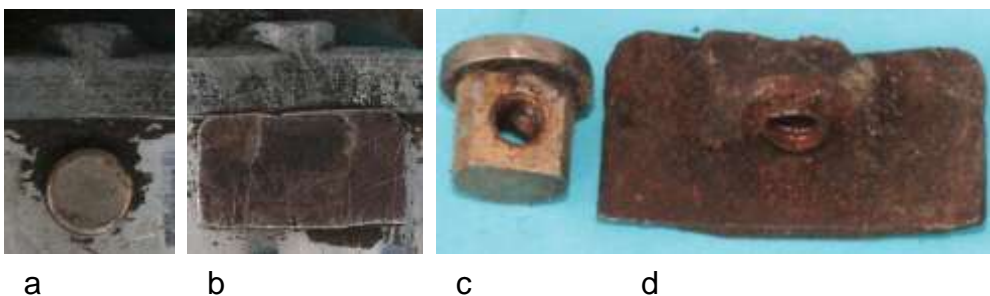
Verschraubung der Gehäuseteile: a) Originalverschraubung, b) Trägerblech der Behelfsmutter, c) Gewindebolzen mit Innengewinde, d) Behelfsmutter
